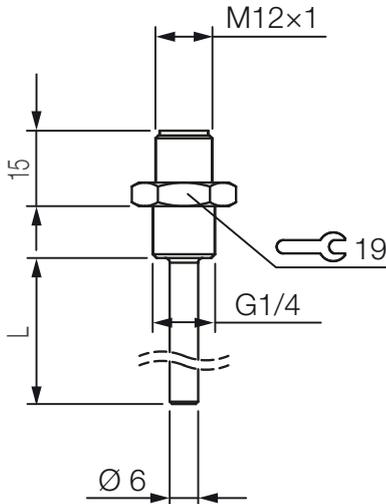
Prozessanschluss mit zylindrischem Gewinde
